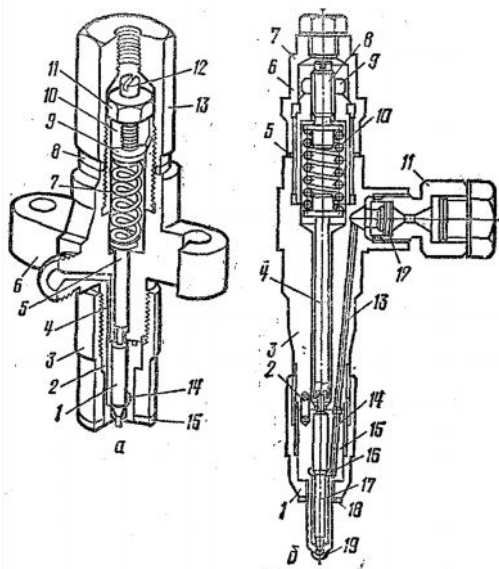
Форсунки: а – штифтова: 1 – голка розпилювача; 2 – корпус розпилювача; 3 – гайка кріплення розпилювача; 4 – канал; 5 – штанга; 6 – корпус форсунки; 7 – пружина; 8 і 15 – прокладки; 9 – тарілка регулювального гвинта; 10 – корпус пружини; 11 – контргайка; 12 – регулювальний гвинт; 13 – ковпак; 14 – порожнина в корпусі розпилювача; б – безштифтова; 1 і 6 – гайки; 2 – штифт; 3 – корпус; 4 – штанга; 5 і 18 – прокладки; 7 – ковпак; 8 – регулювальний гвинт; 9 – контргайка; 10 – пружина; 11 – штуцер; 12 – сітчастий фільтр; 13 і 14 – канали; 15 – корпус розпилювача; 16 – виточка; 17 – голка розпилювача; 19 – отвір розпилювача
